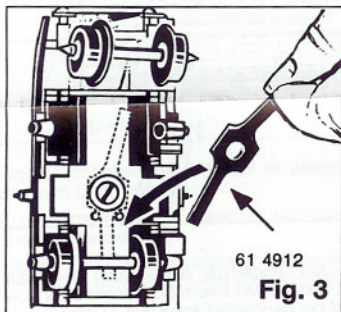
Zum Einsetzen der Stromabnehmerfeder Schraube nicht lösen; nur über den Schraubenkopf legen.
